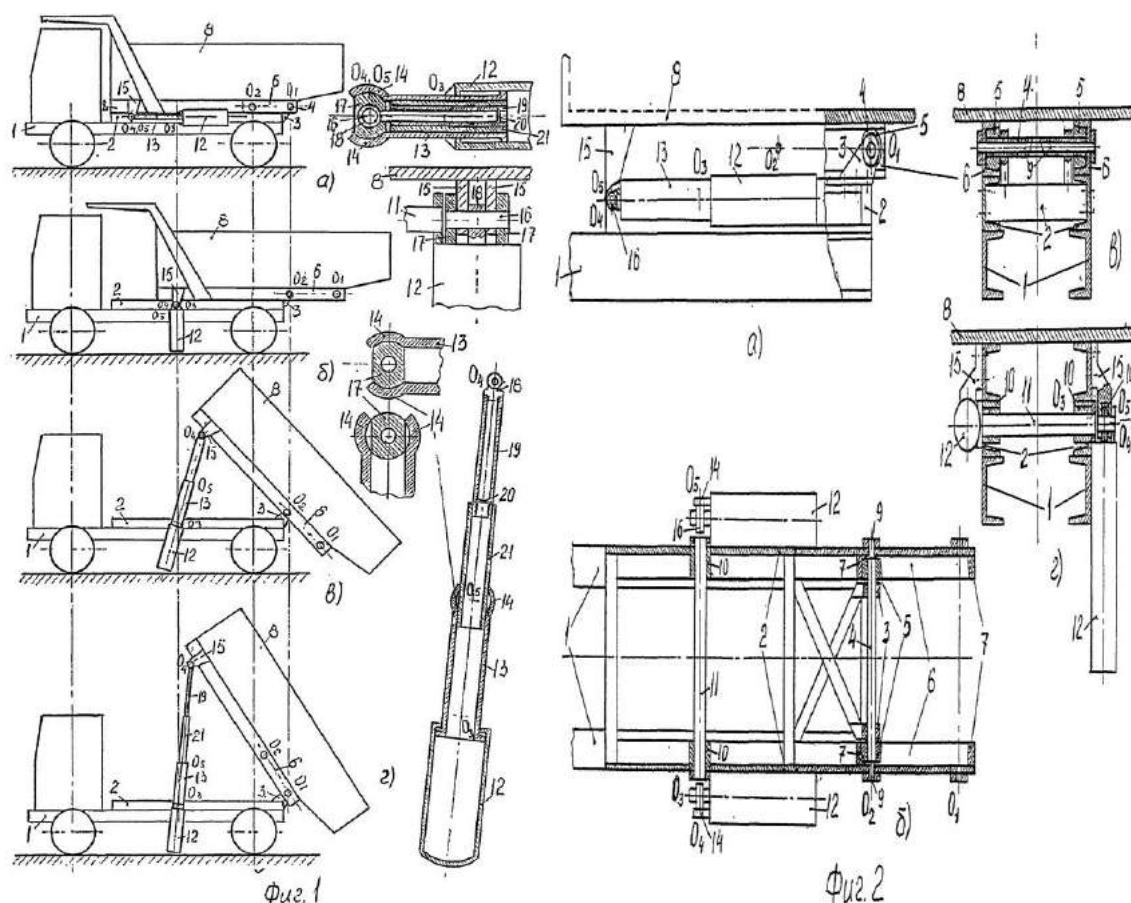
Вид сбоку автосамосвала и вид сбоку гидроподъемный механизм автосамосвала
